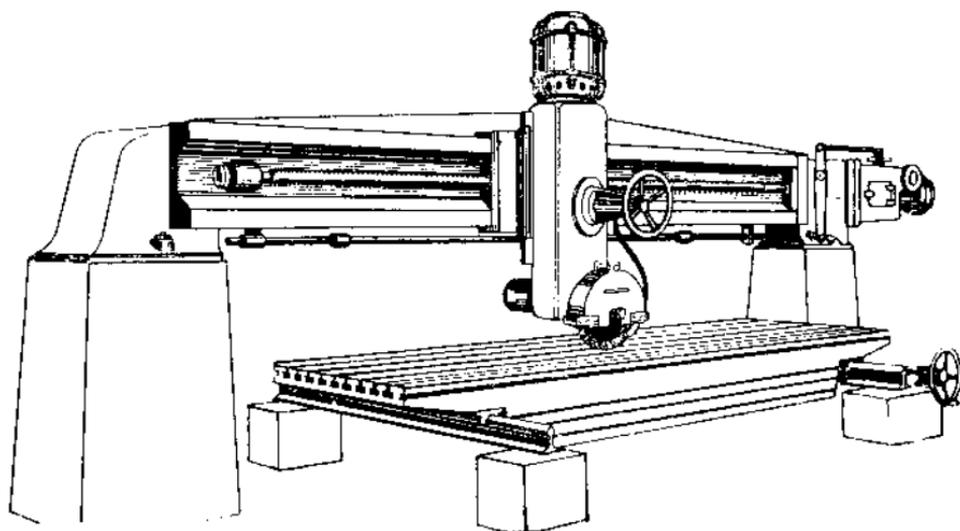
Фрезерный станок «Торпедо» фирмы Вальдрих
